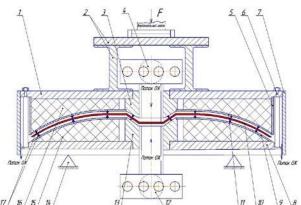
Принципиальная схема устройства закалочного охлаждения дисков: 1 — плита верхняя; 2 фланец; 3 — вставка верхняя; 4 — коллектор верхний; 5 — кожух внутренний; 6 — упор; 7 — кожух наружный; 8 — плита нижняя; 9 — матрица; 10 — заготовка диска; 11 — пуансон; 12 — коллектор нижний; 13 — вставка нижняя;14 — опора; 15 — плита монтажная нижняя; 16 — плита монтажная верхняя; 17 — фиксатор
